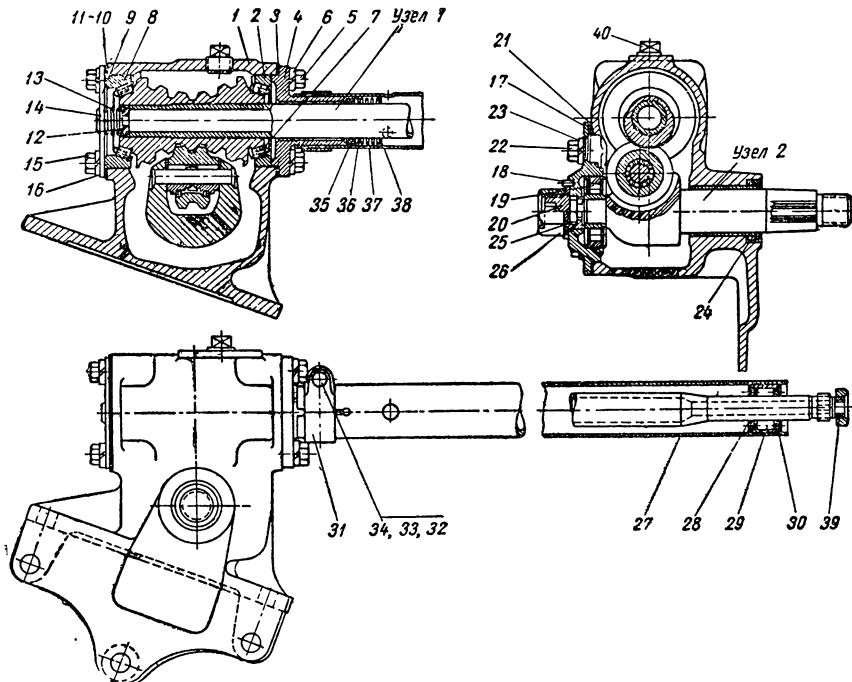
Общая сборка рулевого управления из узлов и деталей
